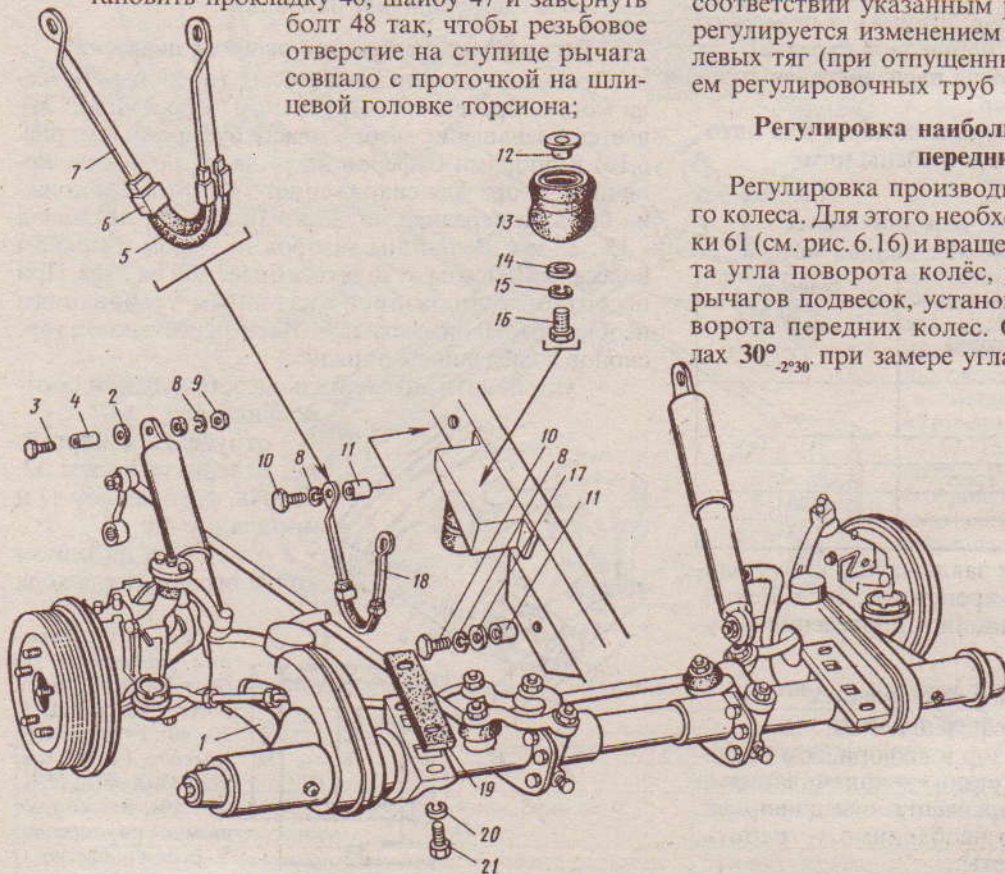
Подвеска передняя: 1 - подвеска передняя в сборе; 2 - втулка шарниров амортизаторов; 3 - болт М10; 4 - втулка распорная; 5 - буфер ограничителя хода колеса; 6 - скоба крепления буфера ограничителя хода колеса; 7 - ограничитель хода колеса; 8 - шайба; 9 - гайка М10; 10 - болт М10; 11 - втулка распорная; 12 - шайба опорная буфера; 13 - буфер подвески; 14 - шайба специальная; 15 - шайба; 16 - болт М8; 17 - шайба ограничительная; 18 - ограничитель хода колеса; 19 - прокладка; 20 - шайба; 21 - болт М16
